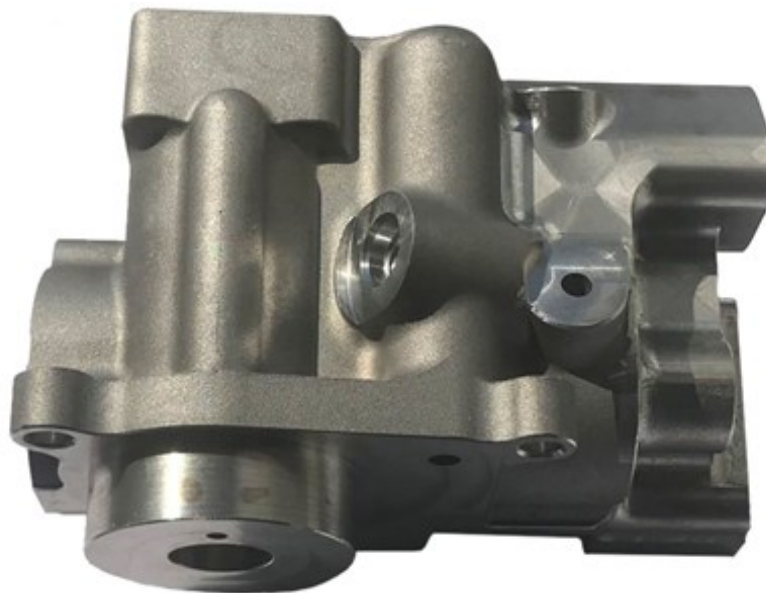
Корпус агрегату авіаційного двигуна
